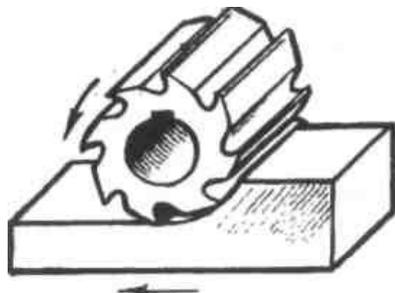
Схема фрезерования цилиндрической фрезой.
